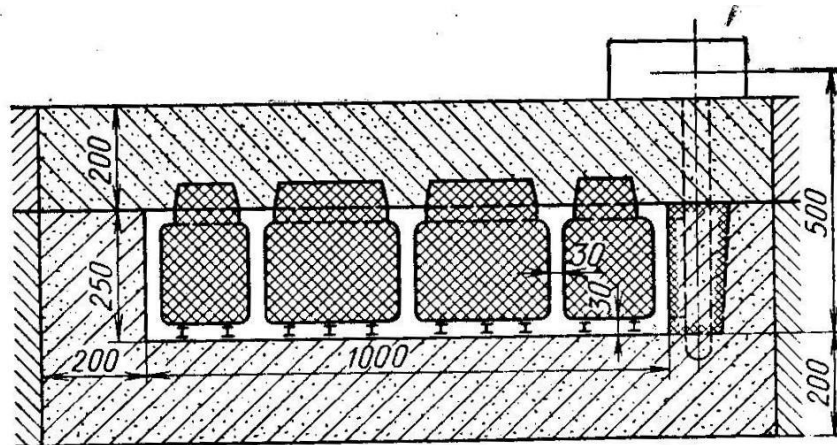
Схема поздовжнього розрізу форми для виливка стола фрезерного верстата
